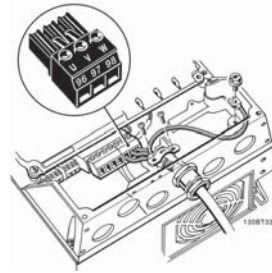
Motoranschluss für Baugröße A5 (IP55/66/NEMA 12)
